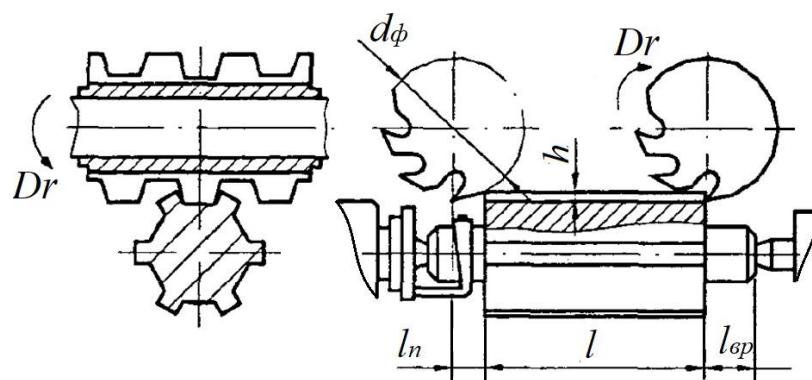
Фрезерування шліців черв'ячною фрезою [24]
